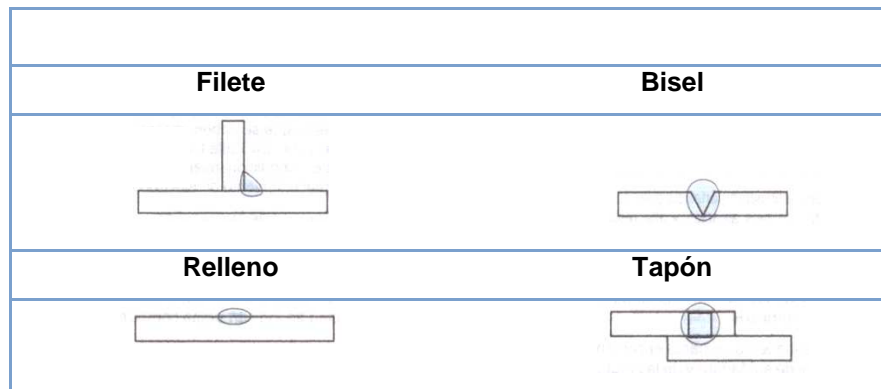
TIPOS DE SOLDADURA
